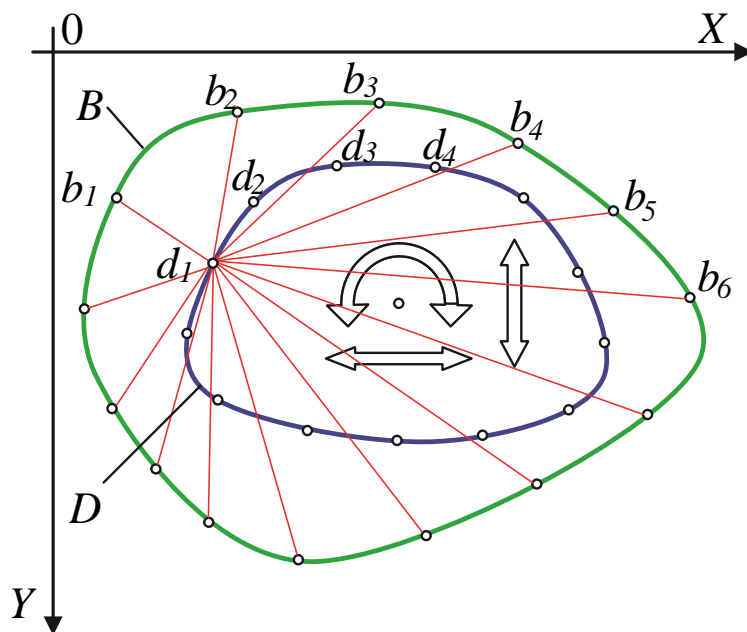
Приклад віртуального базування за контурного фрезерування [136]: D – контур деталі, B – контур заготовки
